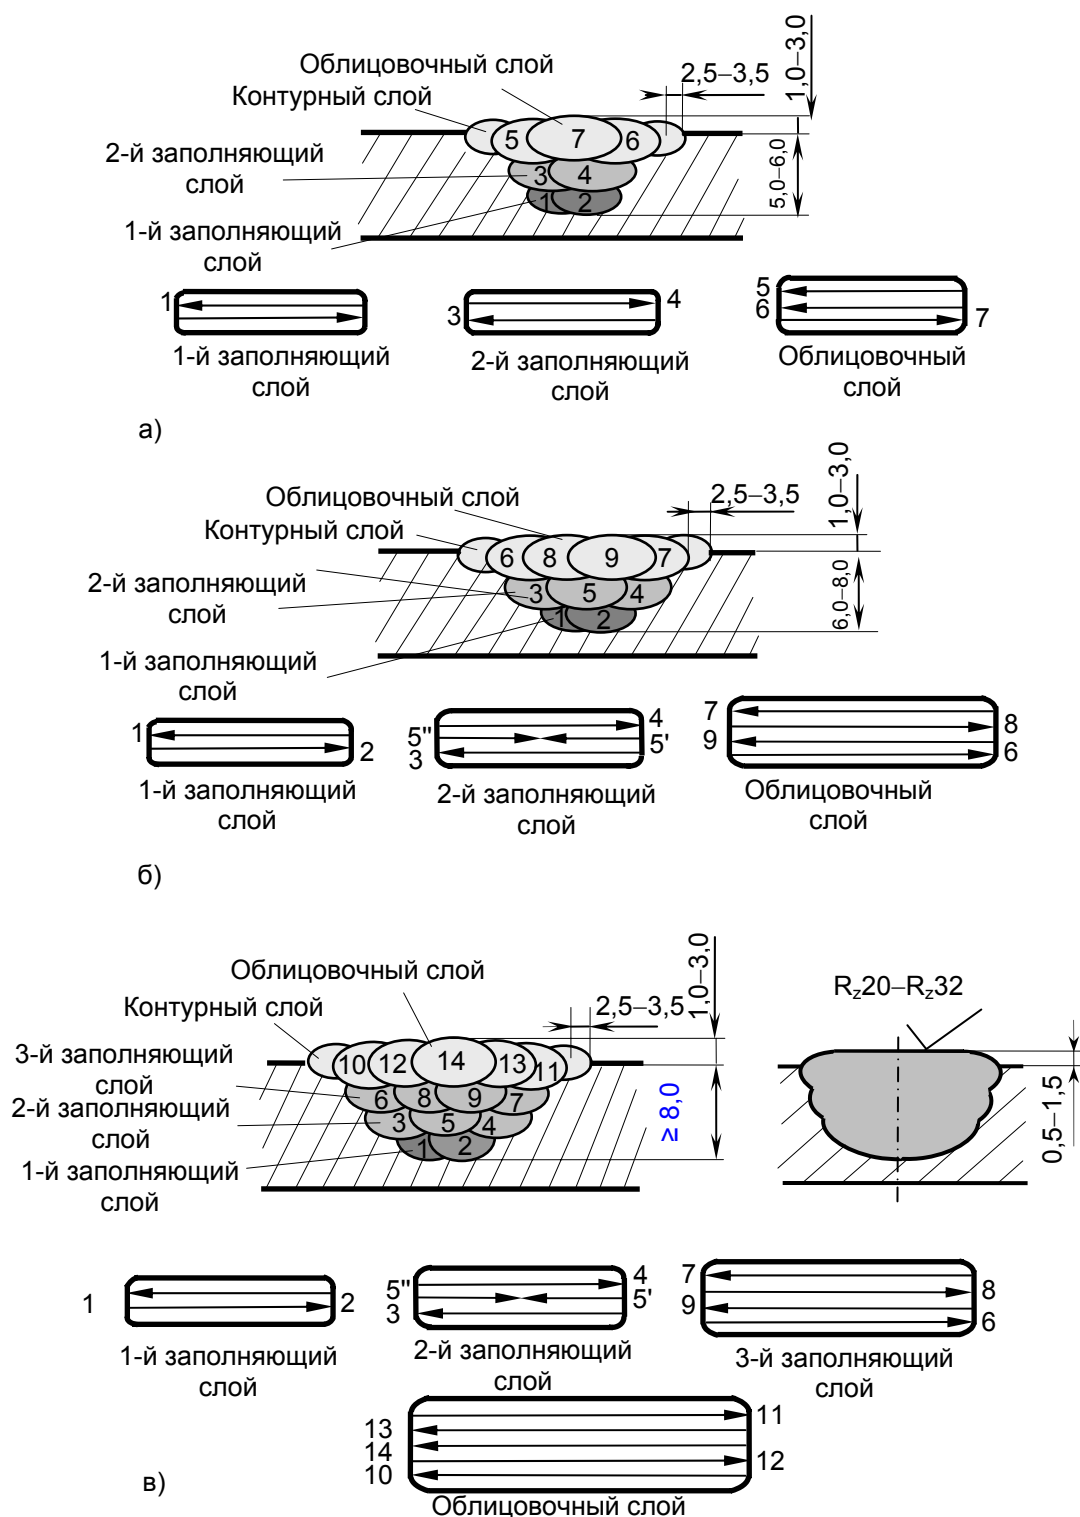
Рекомендуемая последовательность и направление слоев шва при сварке (наплавке) выборки прямолинейной формы
